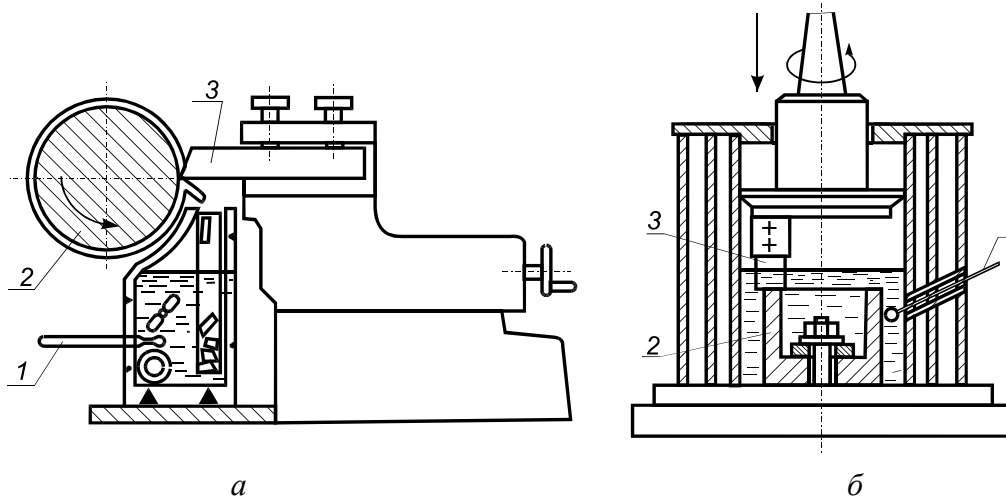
Схемы калориметров: 1 – термометр, 2 – заготовка, 3 – резец
